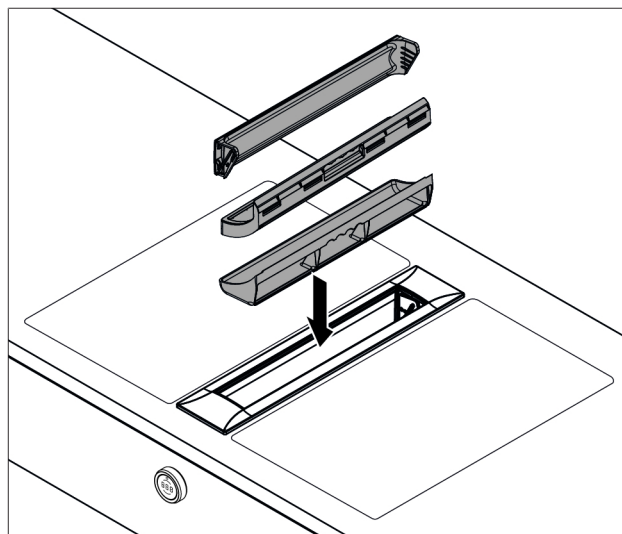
Demontaż komponentów filtra tłuszczowego
